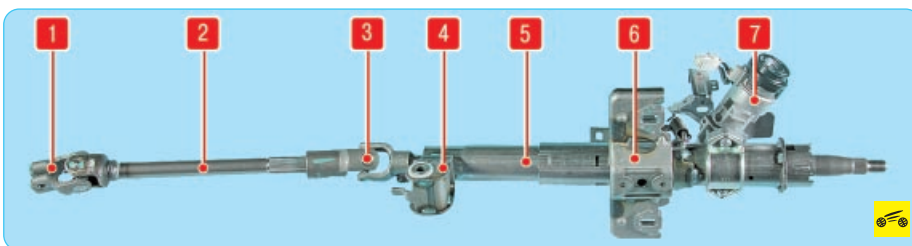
Рулевая колонка: 1 – нижний карданный шарнир промежуточного вала; 2 – промежуточный вал; 3 – верхний карданный шарнир промежуточного вала; 4, 6 – кронштейны крепления рулевой колонки; 5 – корпус рулевой колонки; 7 – выключатель (замок) зажигания
